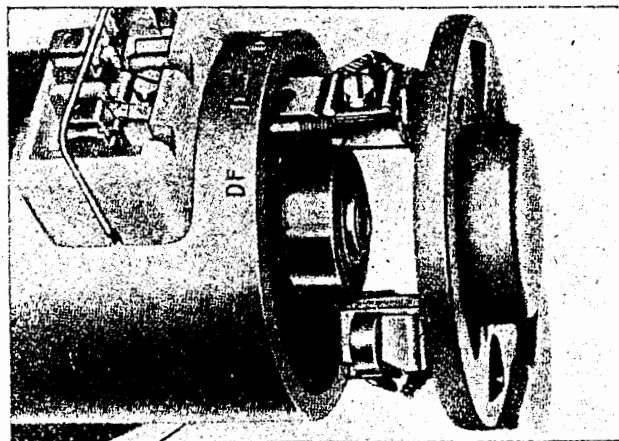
Aufstecken des kollektorseitigen Schildlagers
